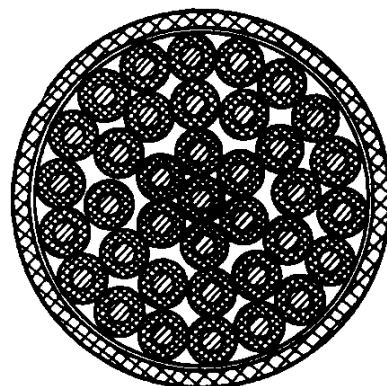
Поперечный разрез 37-жильного кабеля марки СРМ
